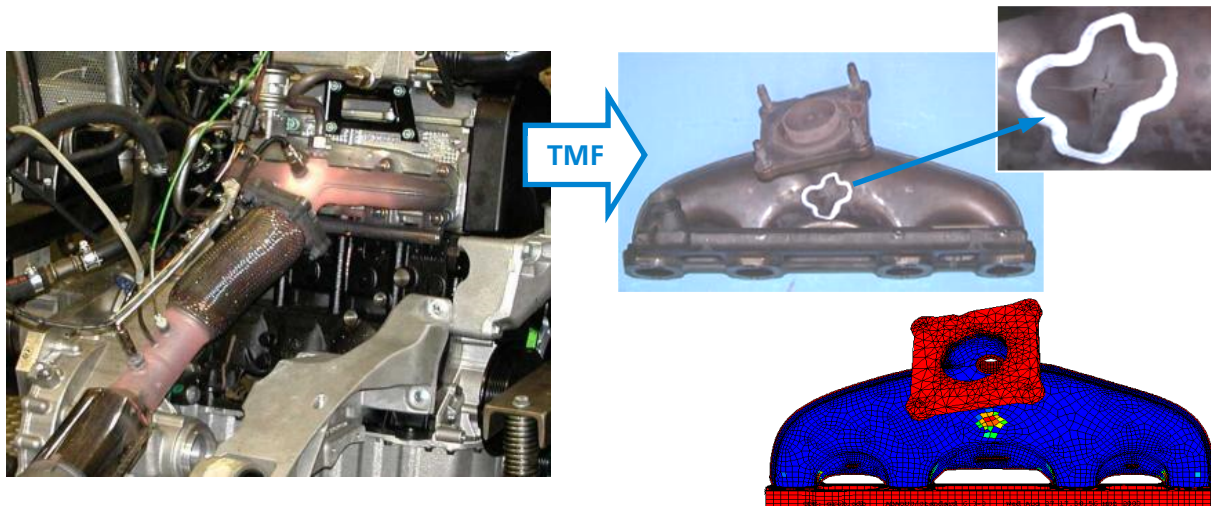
Bauteilversuch, Prüfung einer Abgasanlage und typisches Schadensbild
